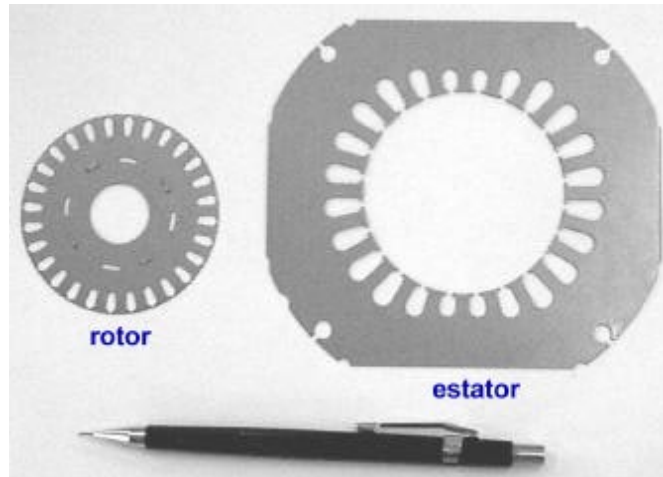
Conjunto de lâminas de um motor para compressor: rotor (esquerda) e estator (direita).
